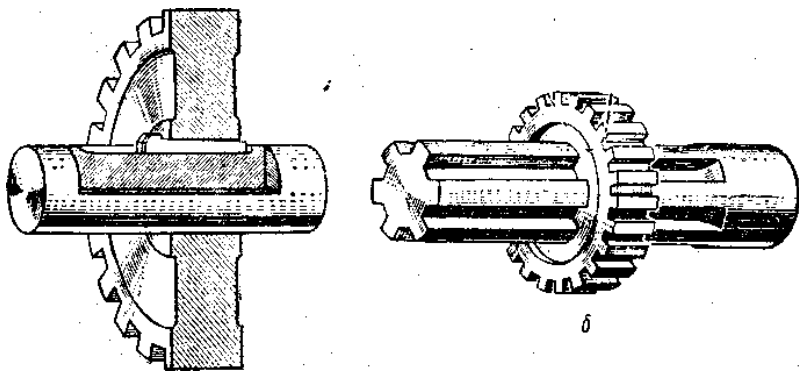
Шпоночное (а) и шлицевое (б) соединения
